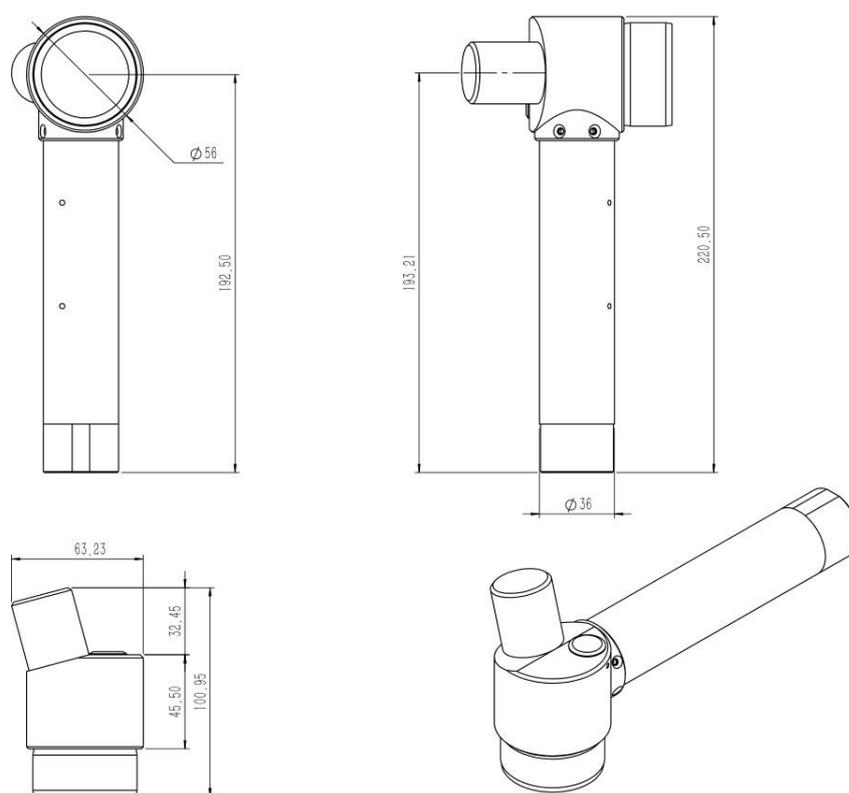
Габаритные размеры лазерной головки для аппаратов CL-50, CL-100.
